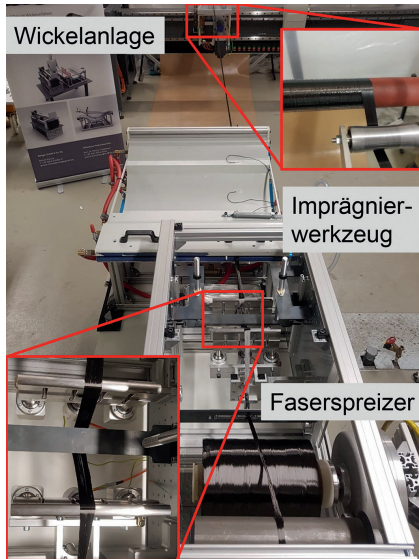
Versuchsanordnung mit Faserspreizer und Imprägnierwerkzeug. Die Detailaufnahmen zeigen einen imprägnierten Roving sowie die gewickelten Probekörper (© TH Köln)
